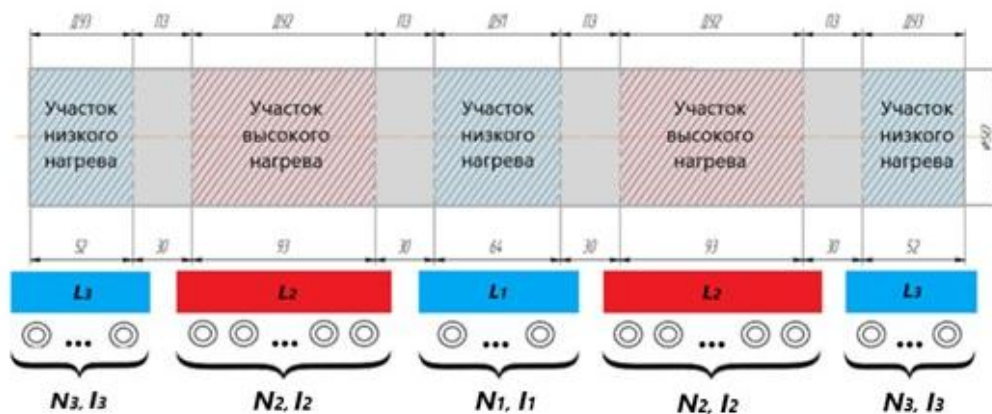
Схема расположения индуктора относительно стальной заготовки
